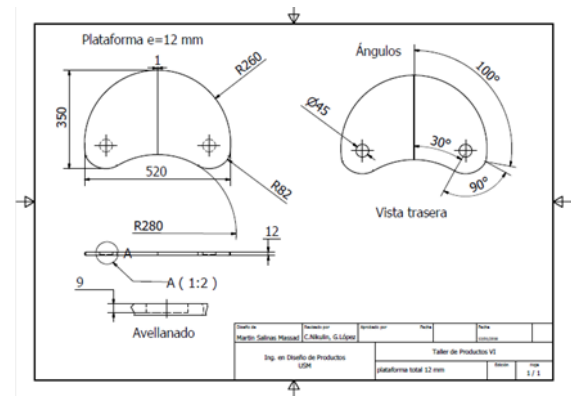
Planimetría de Piezas de base para Mesa Infantil Woodchild
